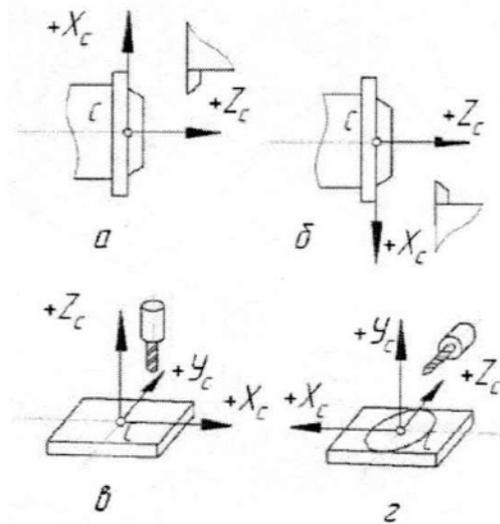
Напрямки стандартної системи координат верстату: а – токарного при переміщенні інструментів над віссю обертання шпинделя; б – те ж, під віссю шпинделя; в, г – свердлильно-розточувальних і фрезерних з відповідно вертикальним і горизонтальним розташуванням шпинделя
